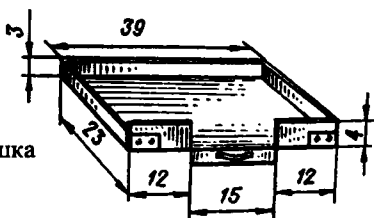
Выдвижная кормушка К. Шломина для нутрий (размеры в см).
